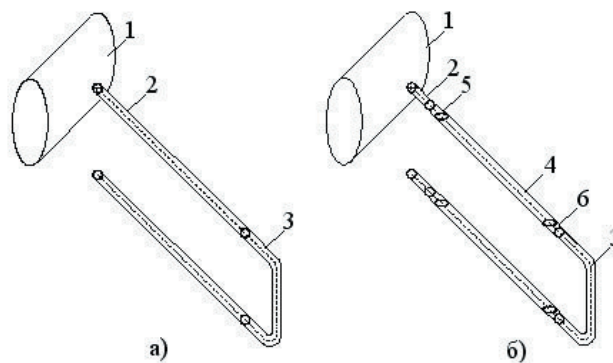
Элемент теплообменной поверхности гладкотрубного регенератора с цилиндрическими (а) и овальными (б) теплообменными трубками: 1 — коллектор; 2 — цилиндрическая трубка; 3 — калач; 4 — овальная трубка; 5 — переходник цилиндр-овал; 6 — переходник овал-цилиндр
